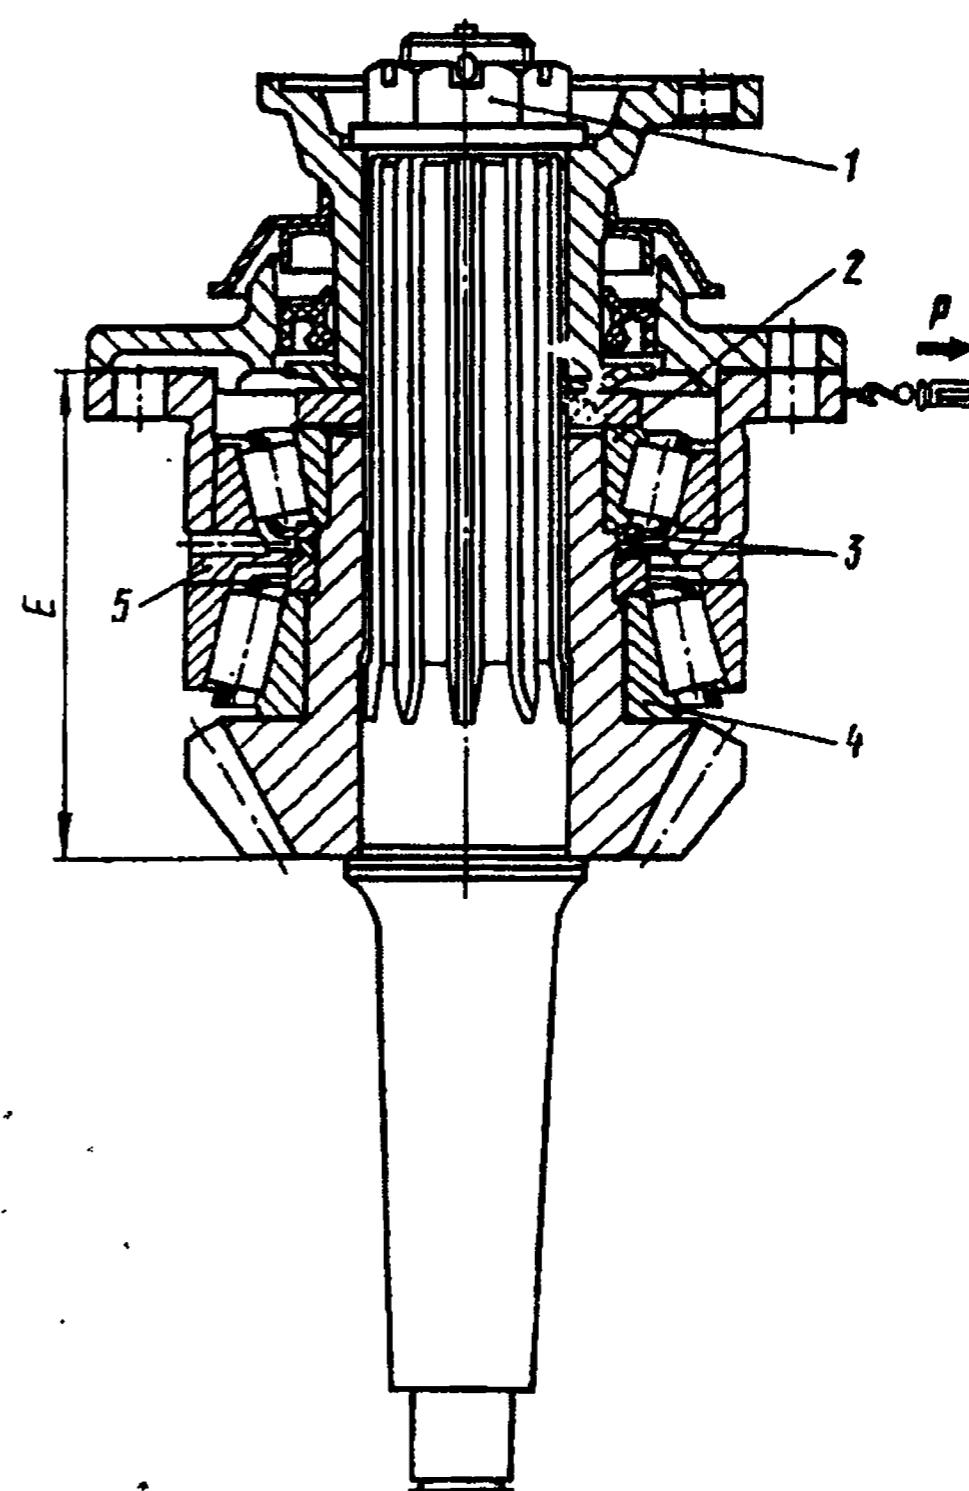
Регулирование подшипников ведущего конического зубчатого колеса:
